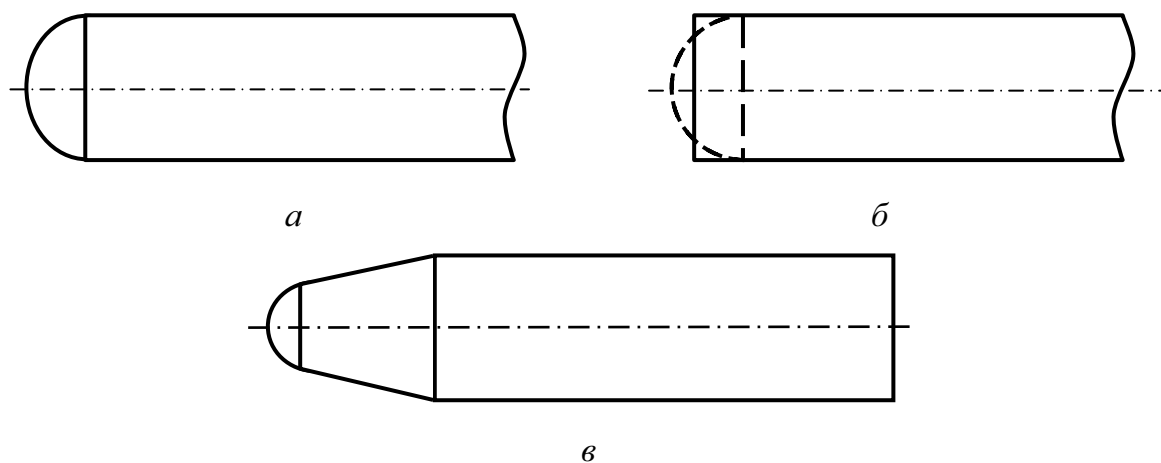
Подготовка вольфрамового электрода для сварки на переменном токе
